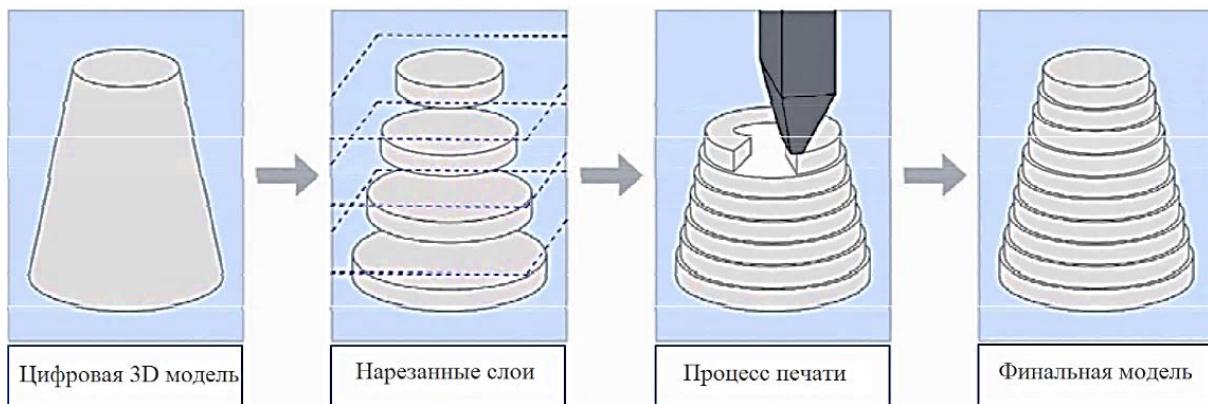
Схема движения экструдера [The flow diagram of the extruder] [6]
